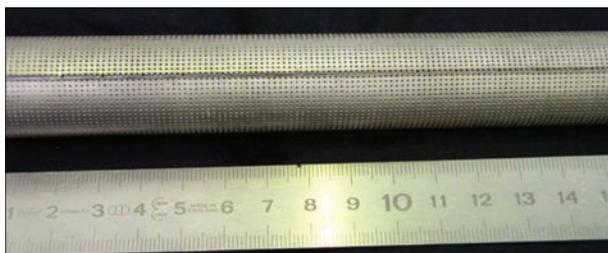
Корпус тонкостенного трубчатого фильтрующего элемента, изготовленного по разработанной технологии лазерной сварки с порошковой присадкой
